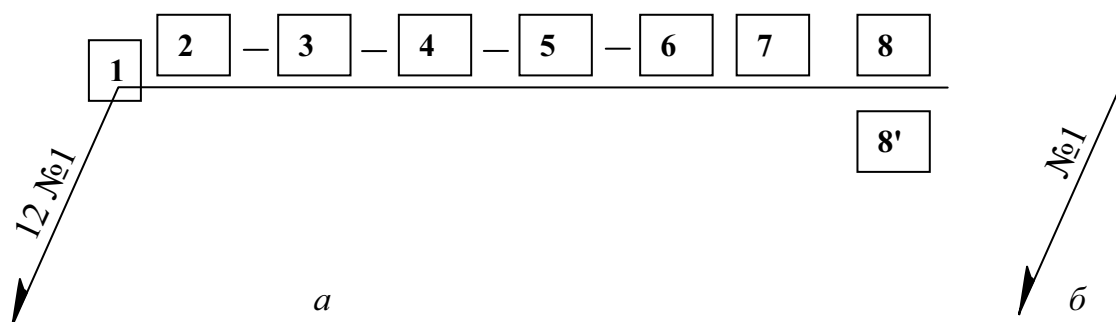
Обозначение сварного шва, выполняемого с невидимой стороны
